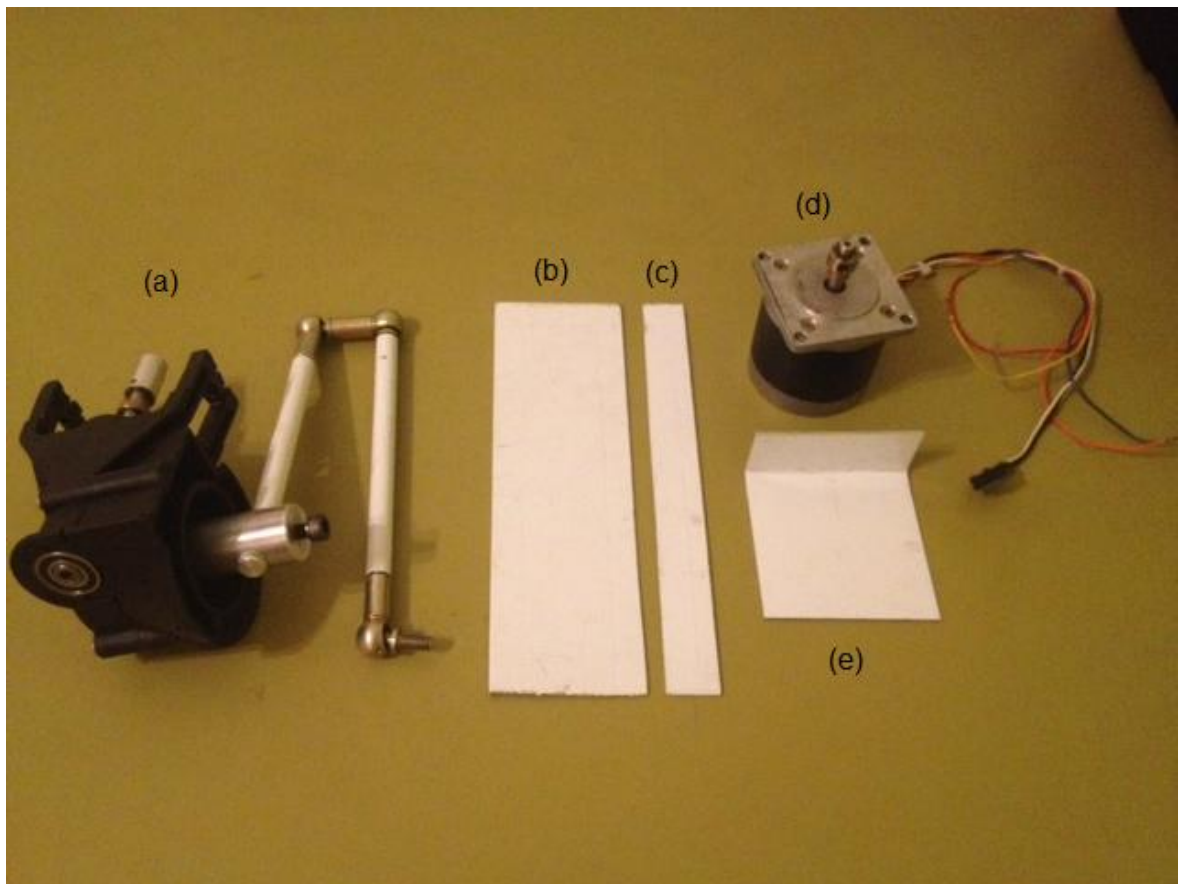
Peças principais do exoesqueleto: (a) caixa de redução e cadeia seriada, (b) placa de fixação dos equipamentos do "braço", (c) placa de fixação dos equipamentos do "antebraço", (d) motor de passo e (e) suporte do motor de passo
